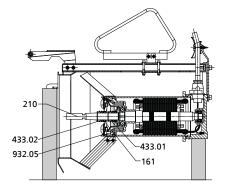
Desmontaje del cierre mecánico en Amaline 200, 300, 400
